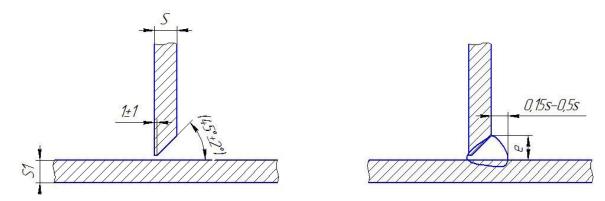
Конструктивные элементы сварного соединения Т6
